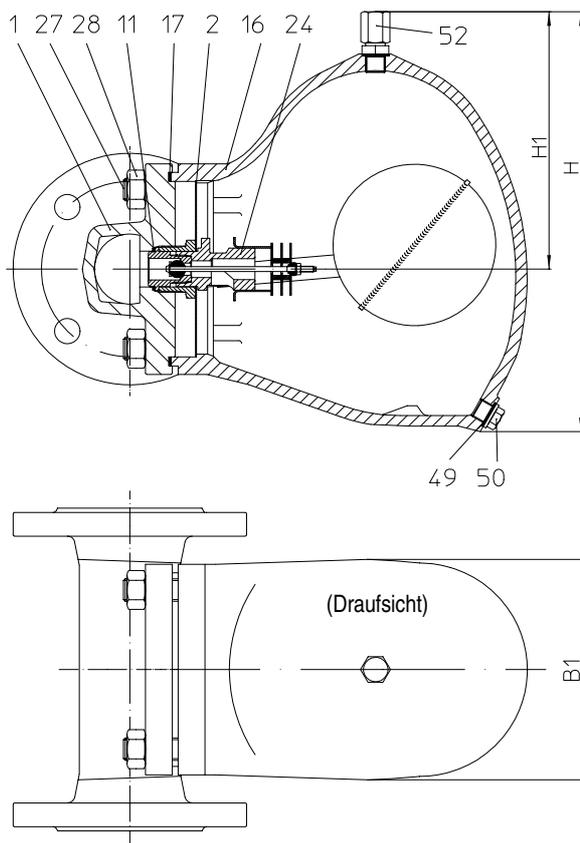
1 mit Flanschen - horizontale Einbaulage
